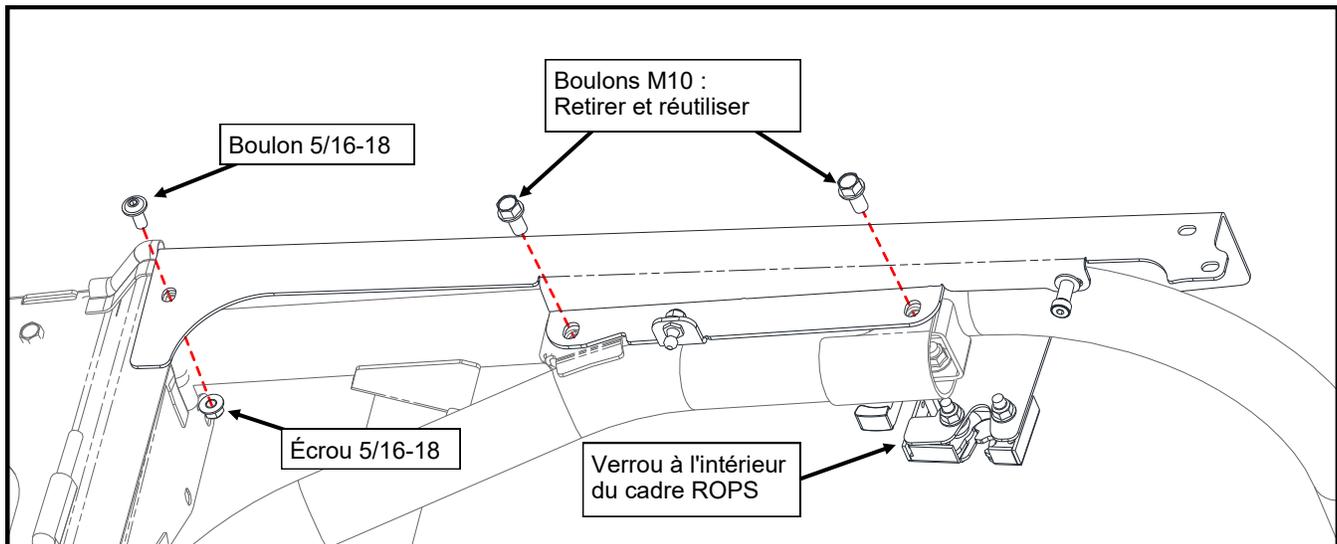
Longerons latéraux arrière (côté conducteur illustré)
